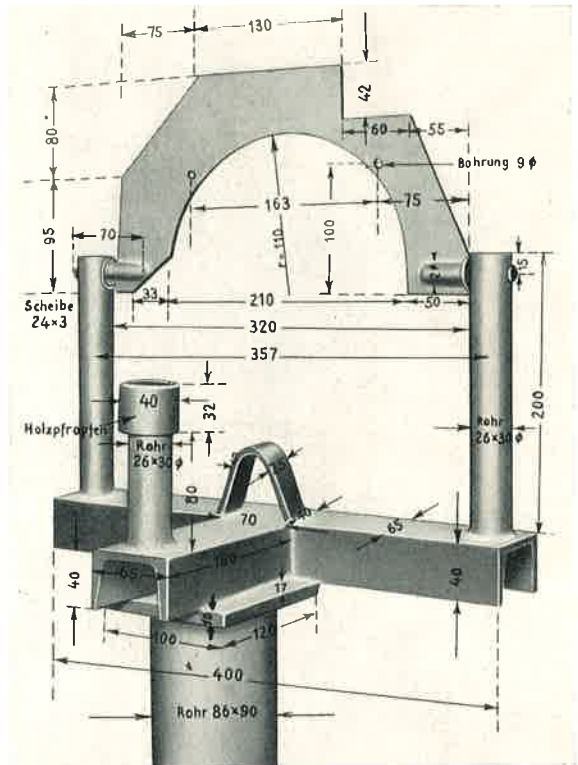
/2: Tisch u. Träger f. Motor u. Getriebe (Bild 4a/4) können mit Werkstattmitteln leicht nachgebaut werden.
